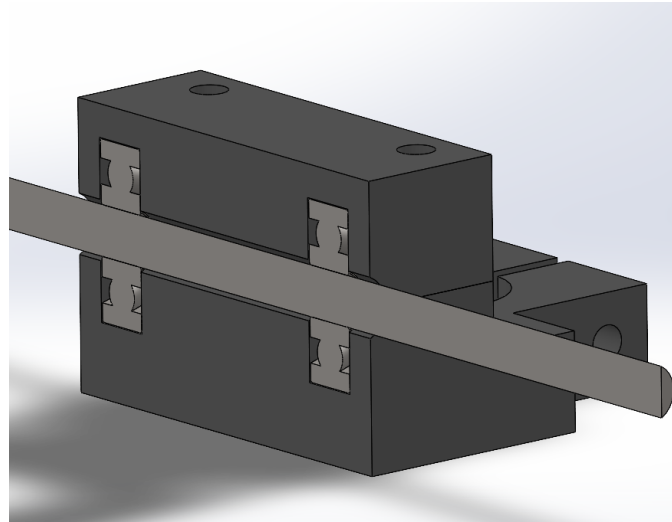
Vista seccionada de la caja y eje de salida.
